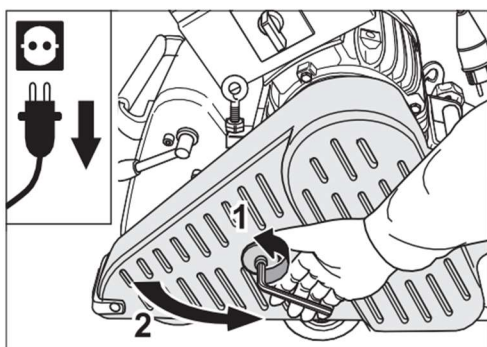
Poluzuj śrubę mocującą i wyciągnij całe tylne koło z obudowy maszyny. Podczas montażu ustaw płaską powierzchnię zaciskową osi w kierunku śruby.
